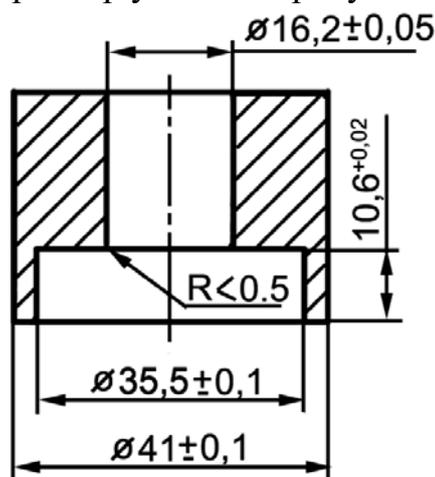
Основные конструктивные размеры оправки для запрессовки уплотнения водяного насоса
